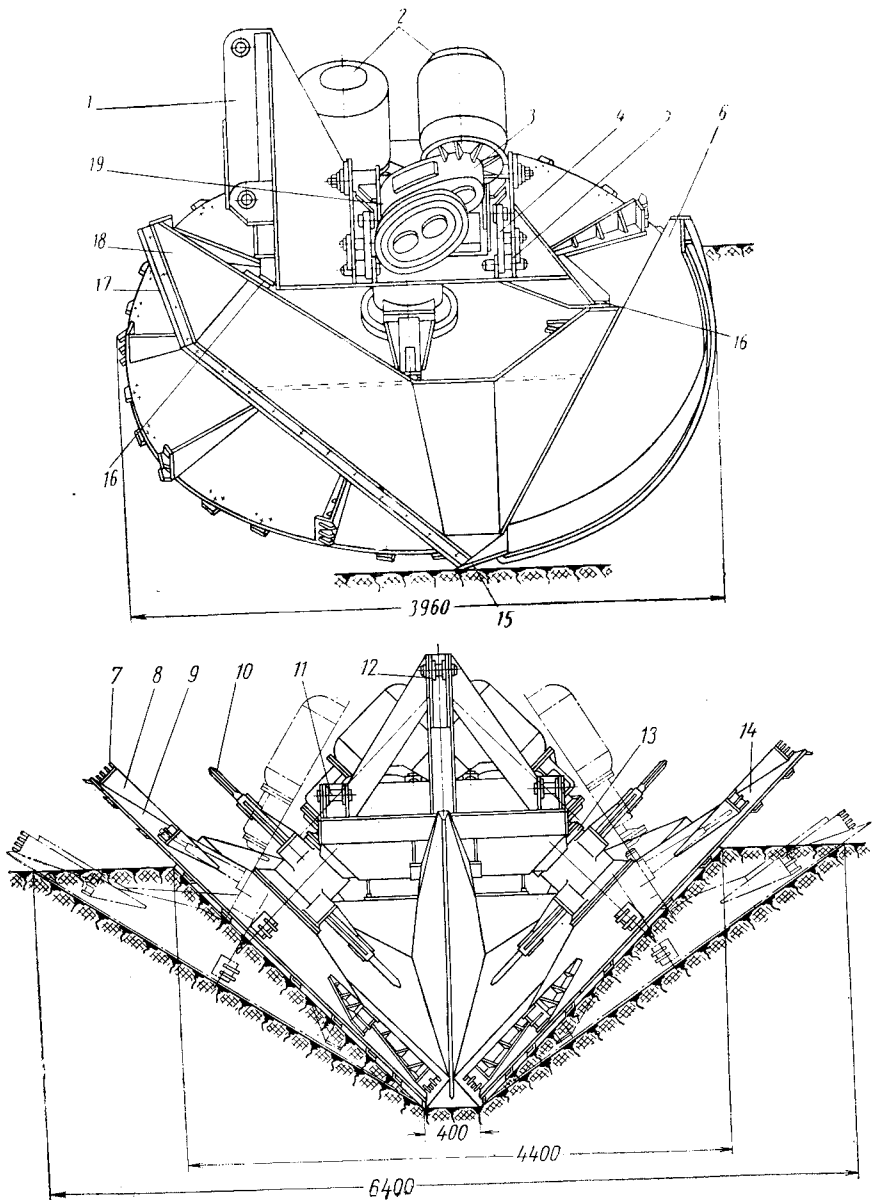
Рабочий орган экскаватора-каналокопателя Д-583:
